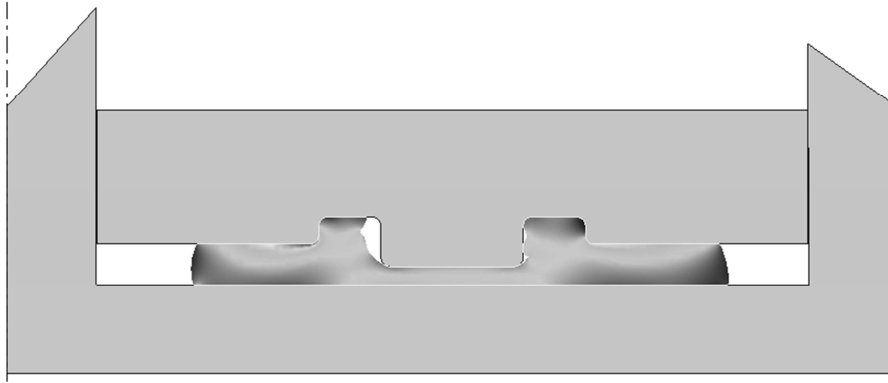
Розміщення низької заготовки по центру верхнього пуансона
